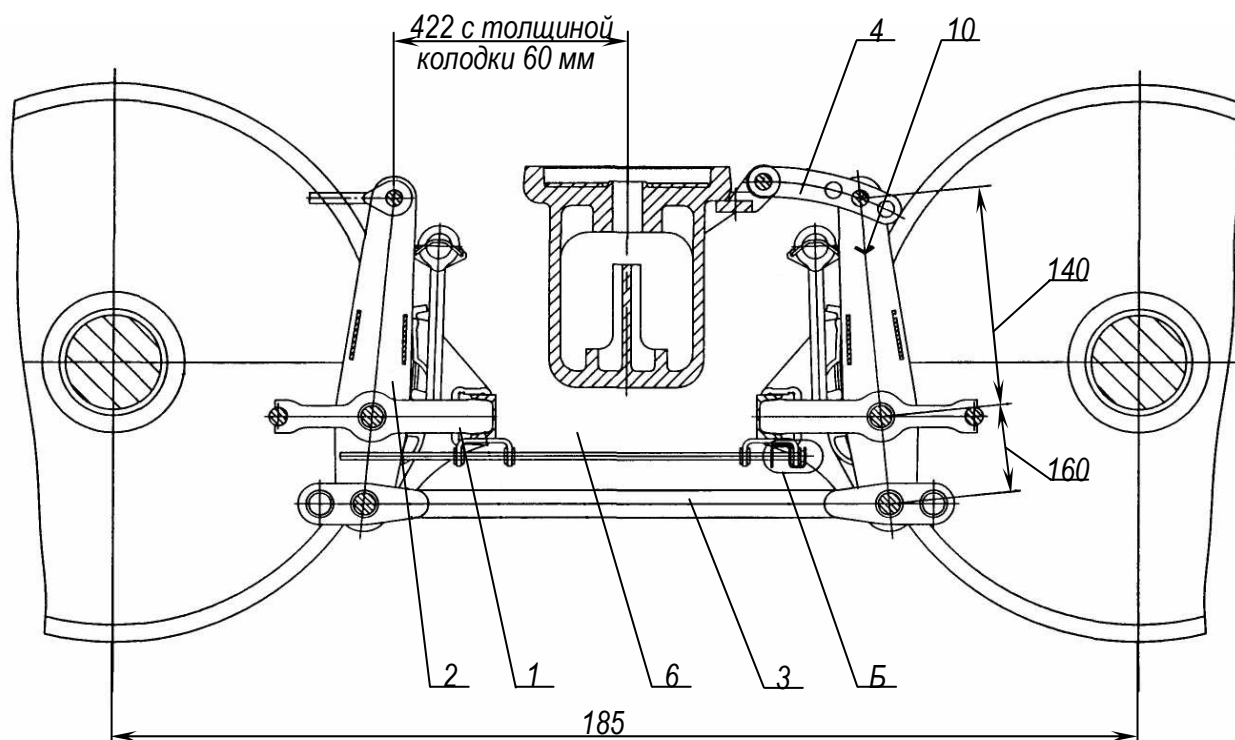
Тормозная рычажная передача: 1 – триангель; 2 – рычаг; 3 – затяжка; 4 - серьга мертвой точки; 5 – предохранитель; 6 - устройство направленного отвода колодок; 7 – втулка; 8 – скоба; 9 – кронштейн; 10 - предохранитель
